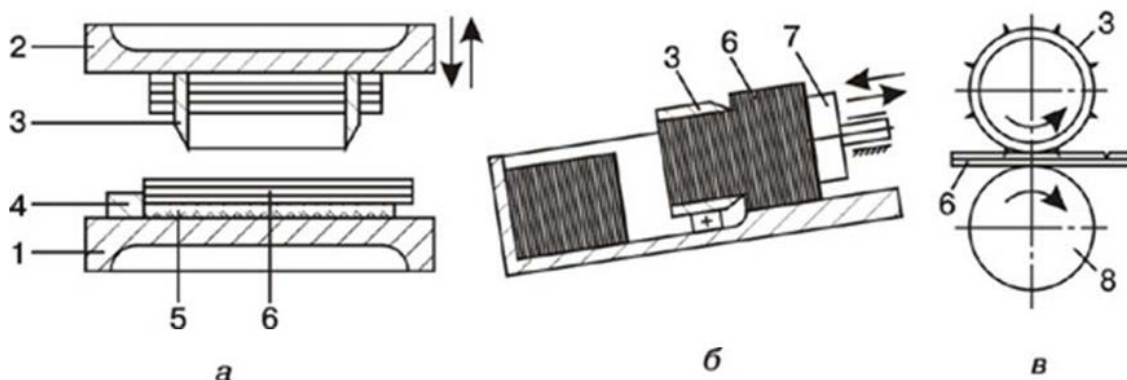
Схемы устройств высечки по принципу ножевого резания:
